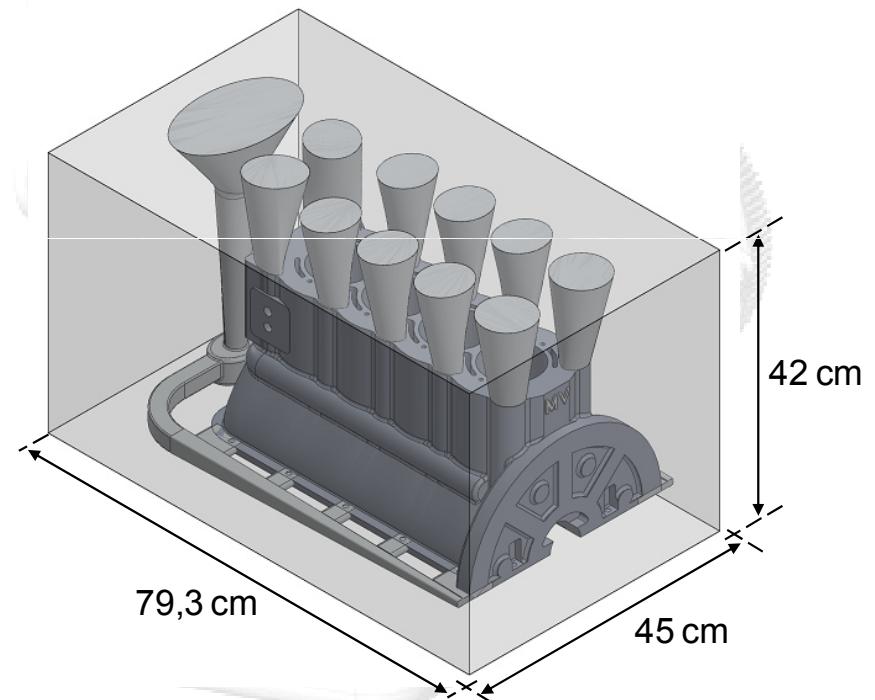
DISEÑO METALÚRGICO DEL MOLDE EN ARENA SECA
